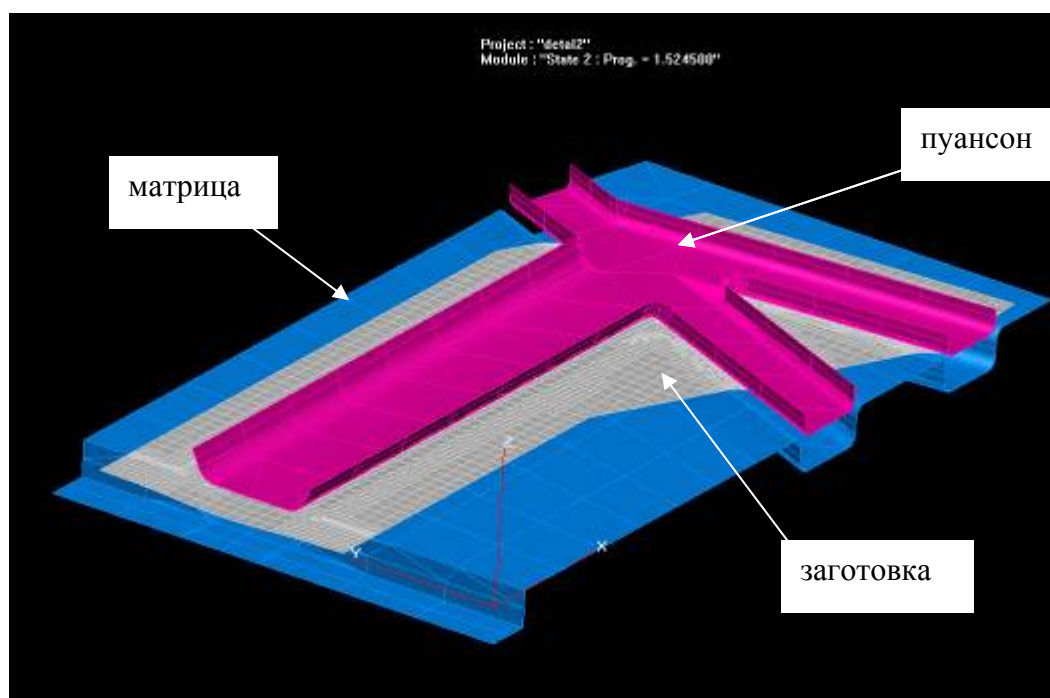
Конечно-элементные модели инструмента и заготовки:
